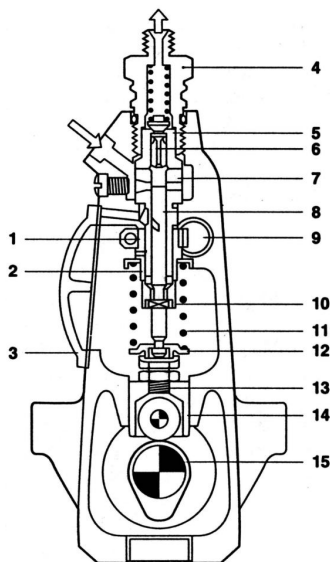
Секция рядного ТНВД: 1 – зубчатый сектор; 2 – регулирующая поворотная втулка плунжера; 3 – боковая крышка; 4 – штуцер нагнетательного клапана; 5 – корпус нагнетательного клапана; 6 – нагнетательный клапан; 7 – гильза плунжера; 8 – плунжер; 9 – рейка ТНВД; 10 – поводок плунжера; 11 – возвратная пружина плунжера; 12 – нижняя тарелка возвратной пружины; 13 – регулировочный болт; 14 – роликовый толкатель; 15 – кулачковый вал
